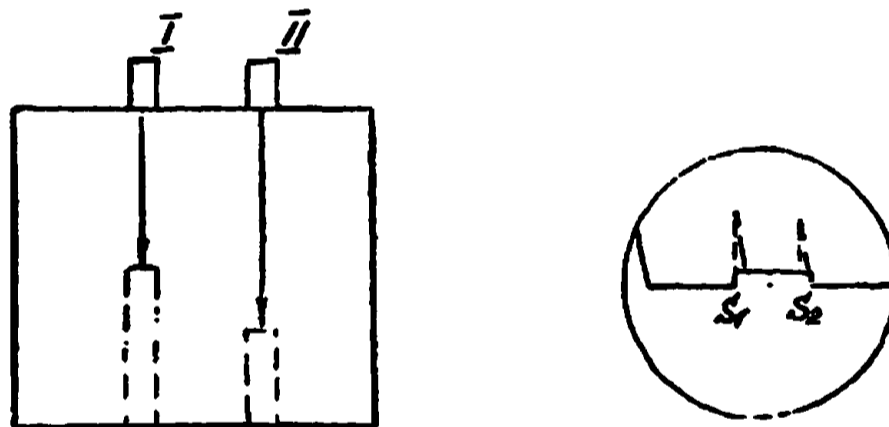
Схема настройки длительности развертки и чувствительности дефектоскопа при контроле прямыми РС ПЭП сварных соединений.
